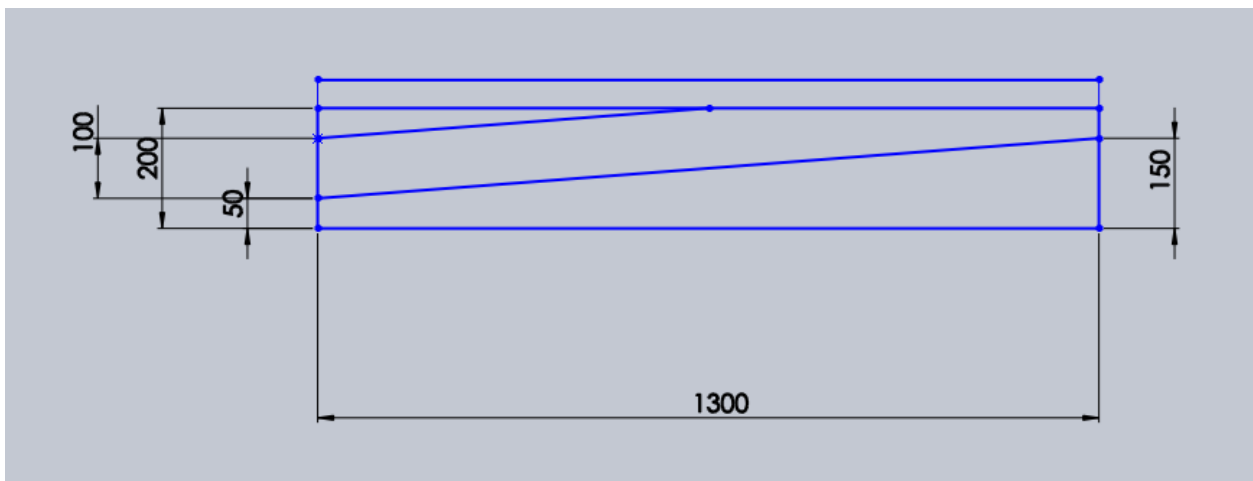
Vista de la plataforma de tijeras en estado replegada.
